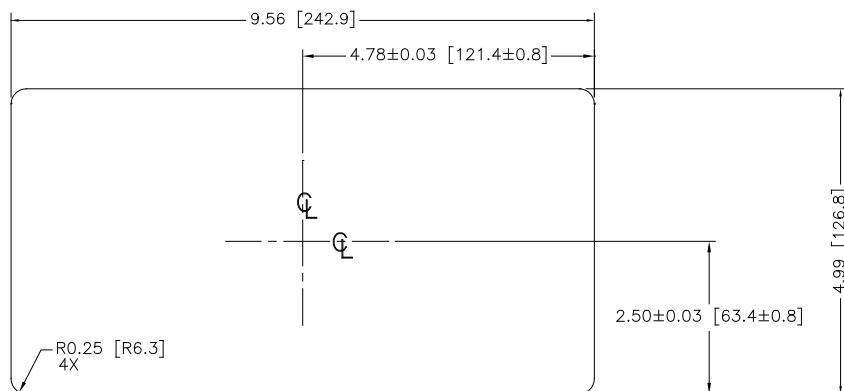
Dimensions de découpe du montage sur tableau de l'IND560
